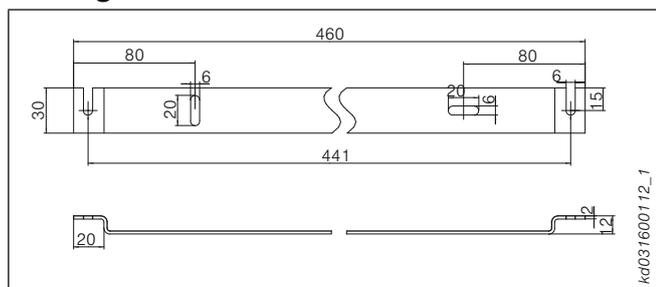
Montagewinkel für externe Montage des Solar-Panels
